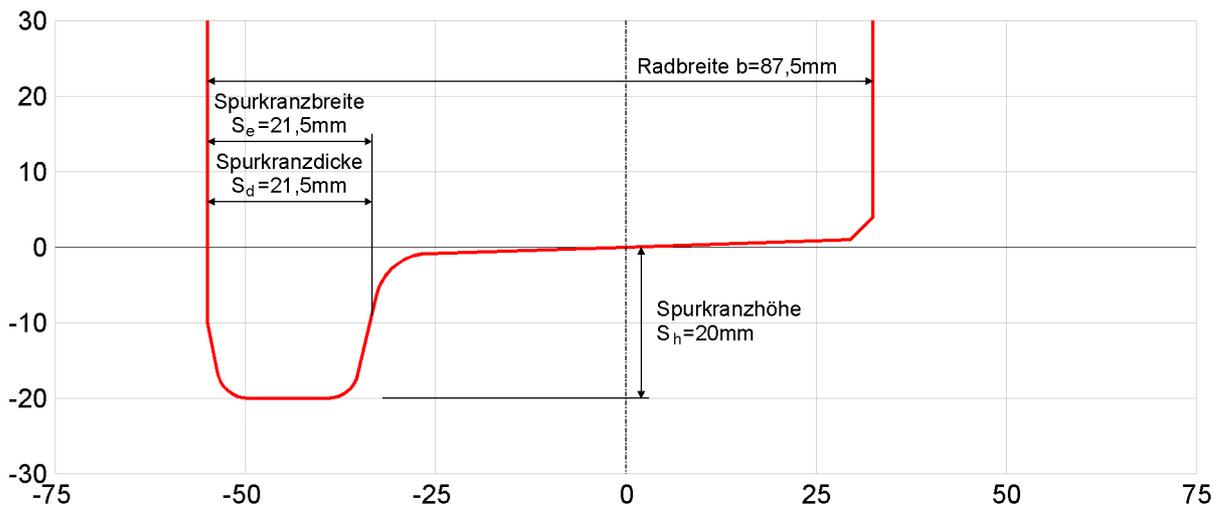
Radprofil Straßenbahn (Typen E_x/c_x)
